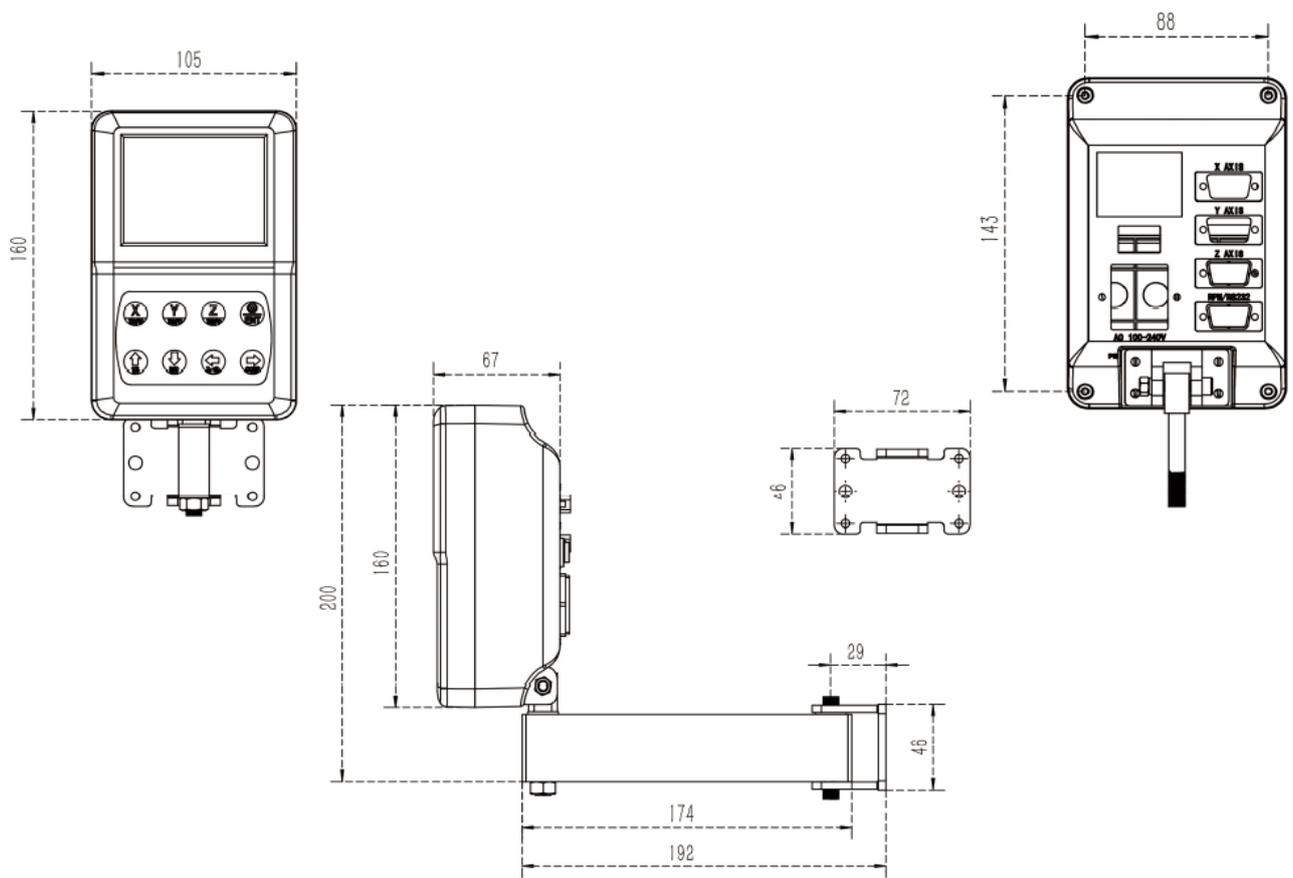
Габаритный чертеж цифрового дисплея DL50.
